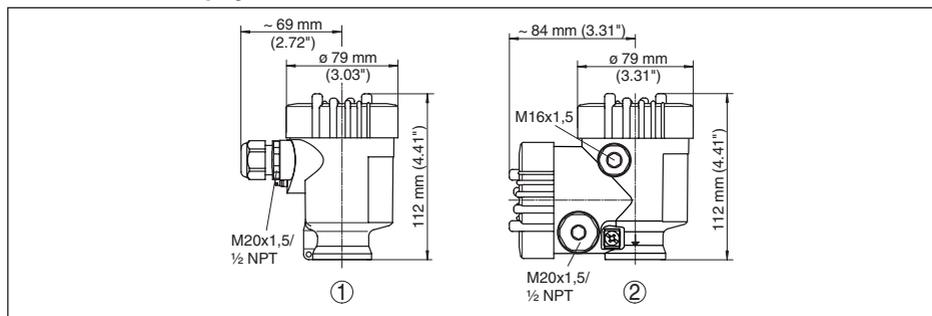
Корпуса в исполнении IP 66/IP 68 (0,2 bar) - с установленным модулем индикации и настройки корпус выше на 9 mm/0.35 in
